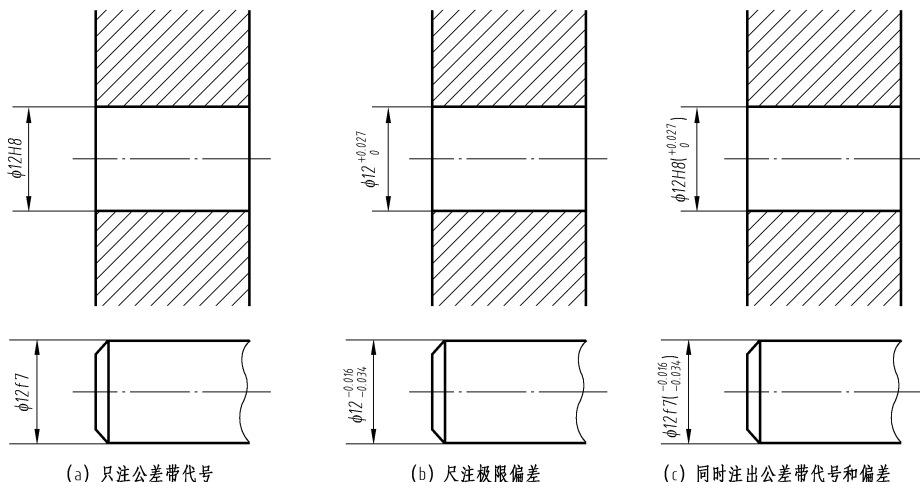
公差带代号、极限偏差在零件图上的标注形式
